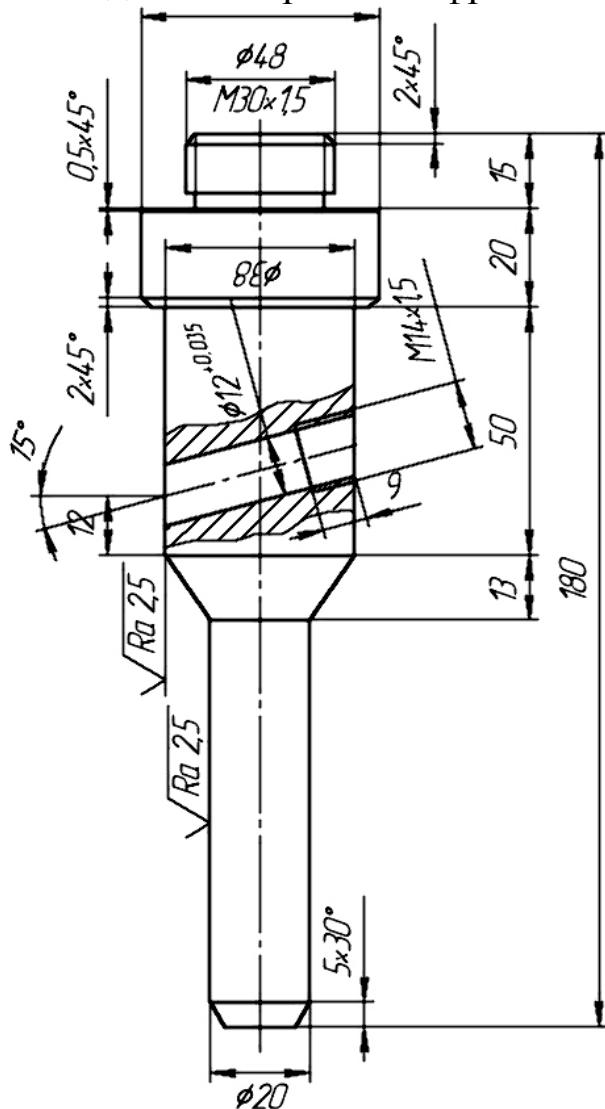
Різцева оправка для обробки фасок клапанних гнізд головки циліндрів
